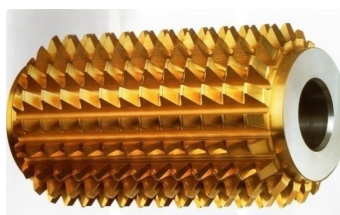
Fresa-mãe ou ferramenta tipo caracol (*HOB*) [22].
